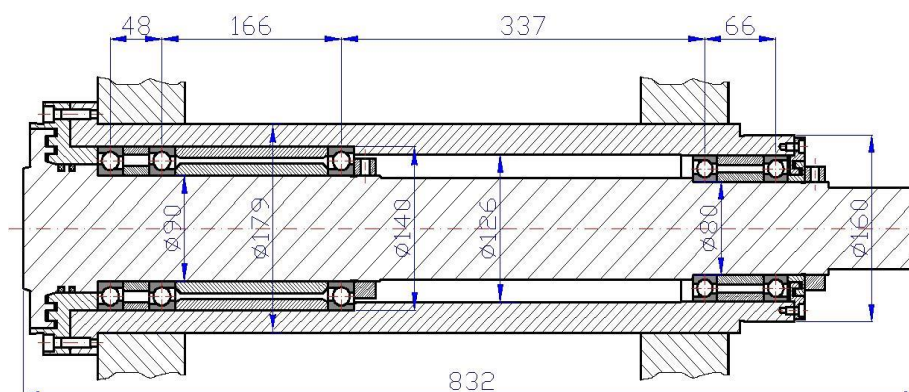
Эскиз шпиндельного узла гильзовой конструкции шлифовального станка
